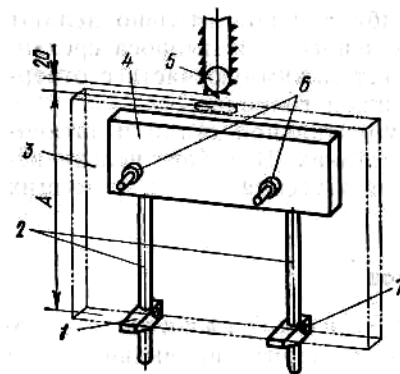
Наладка базирующих упоров цепнодолбежного станка при выборке гнезд в шитовой детали:
